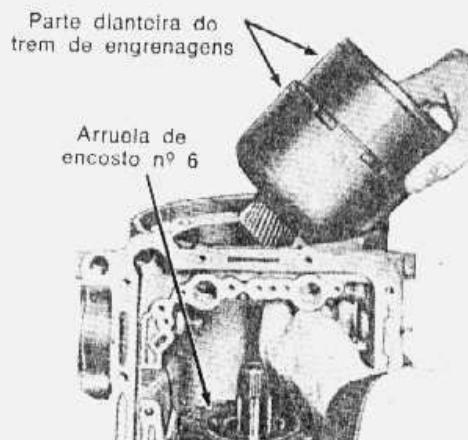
remoção e instalação da parte dianteira do trem de engrenagens
